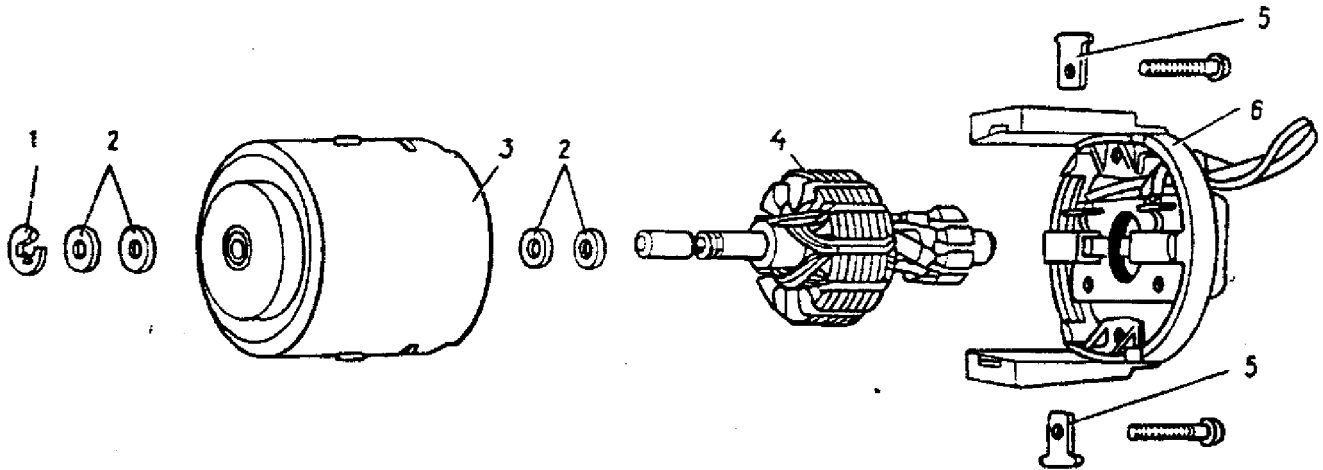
Componentes do motor elétrico da ventilação interna: 1 - arruela de retenção; 2 - arruela; 3 - carcaça; 4 - induzido; 5 - presilha para fixação dos parafusos; 6 - tampa.
